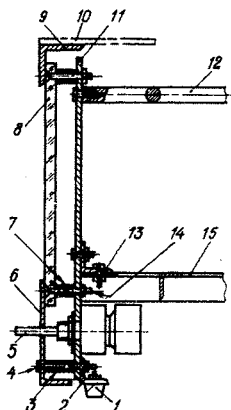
Пример оформления лицевой стороны радиоприемника: 1 — ножка; 2 — уголок-держатель ножек; 3, 7 — трубчатые стойки; 4, 14 — винты; 5 — переменный резистор; 6 — наличник нижний; 8 — шкала, стекло органическое; 9 — наличник верхний; 10 — крышка; 11 — стенка передняя; 12 — стяжка; 13, 15 — уголки.
